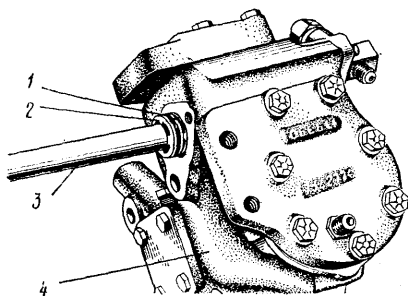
Расположение в компрессоре клапана регулятора давления в испарителе:
